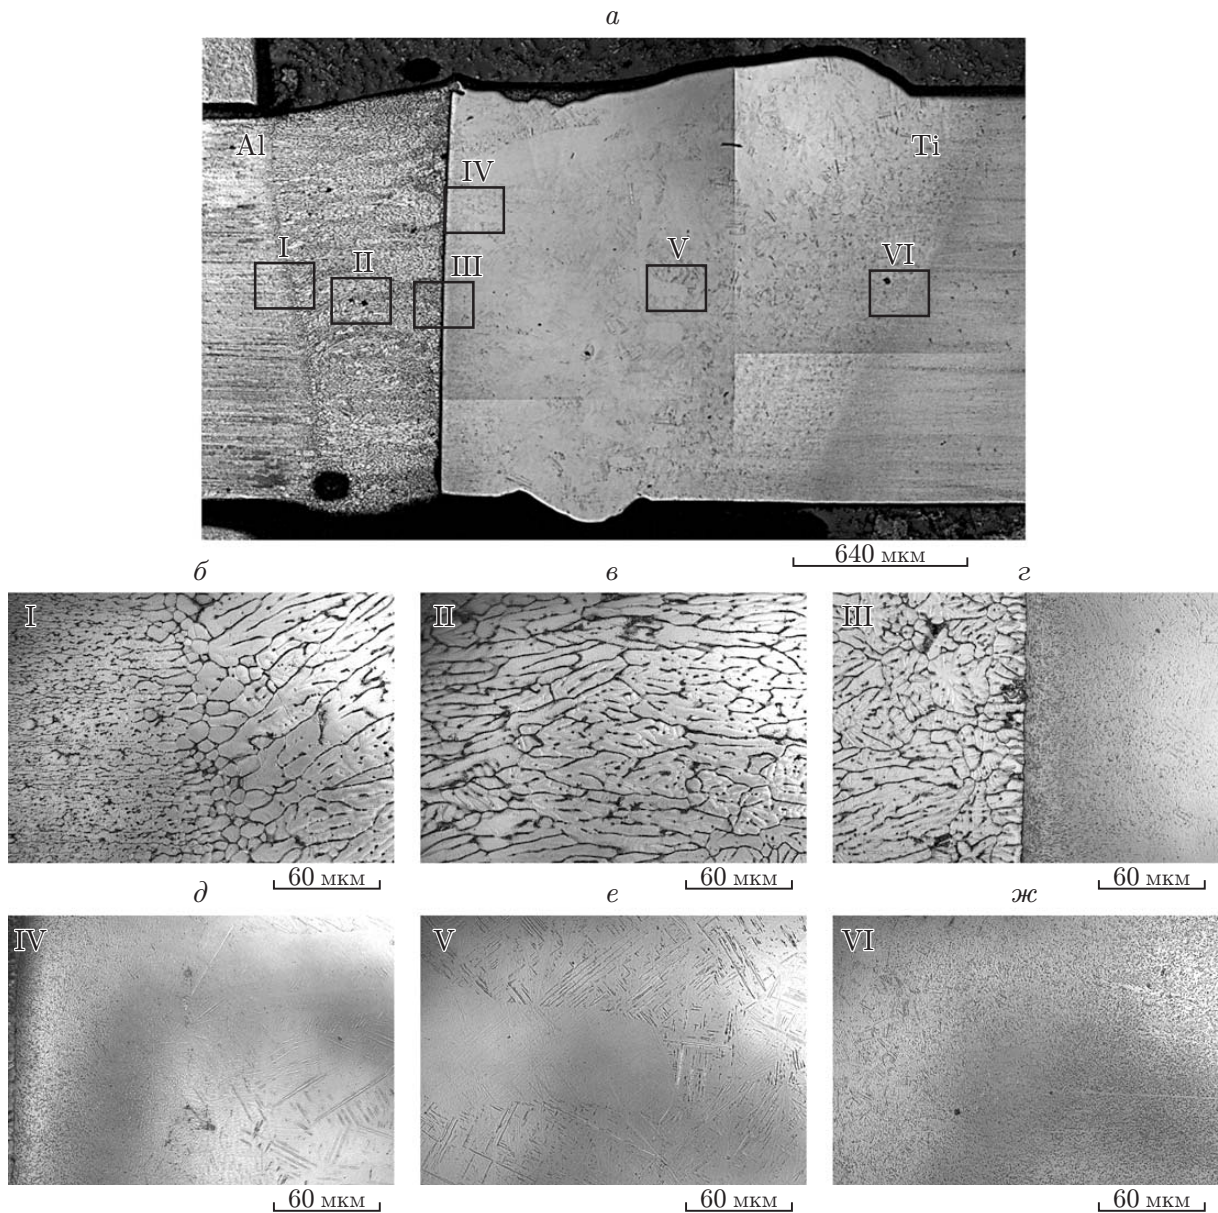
Структура сварного соединения, сваренного со смещением лазерного луча на 1 мм (оптическая металлография):
